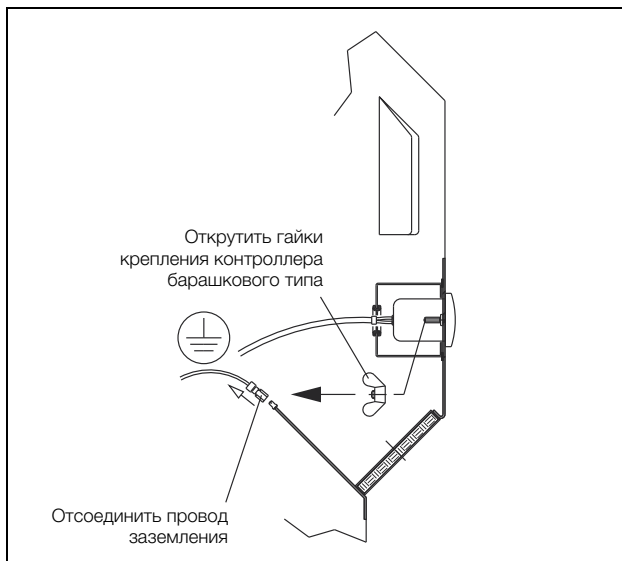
Подготовка к извлечению контроллера (вид сбоку)
